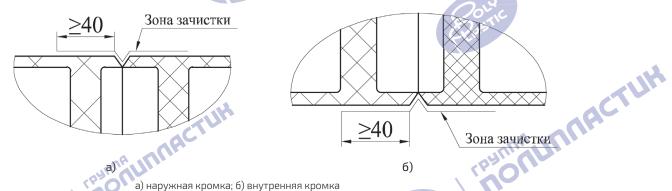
Зачистка поверхности труб перед сваркой
